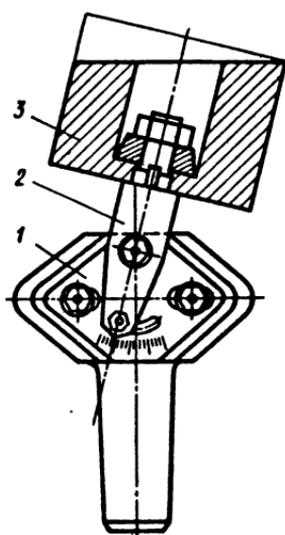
Поворотная оправка для обработки торца детали под углом к оси:
